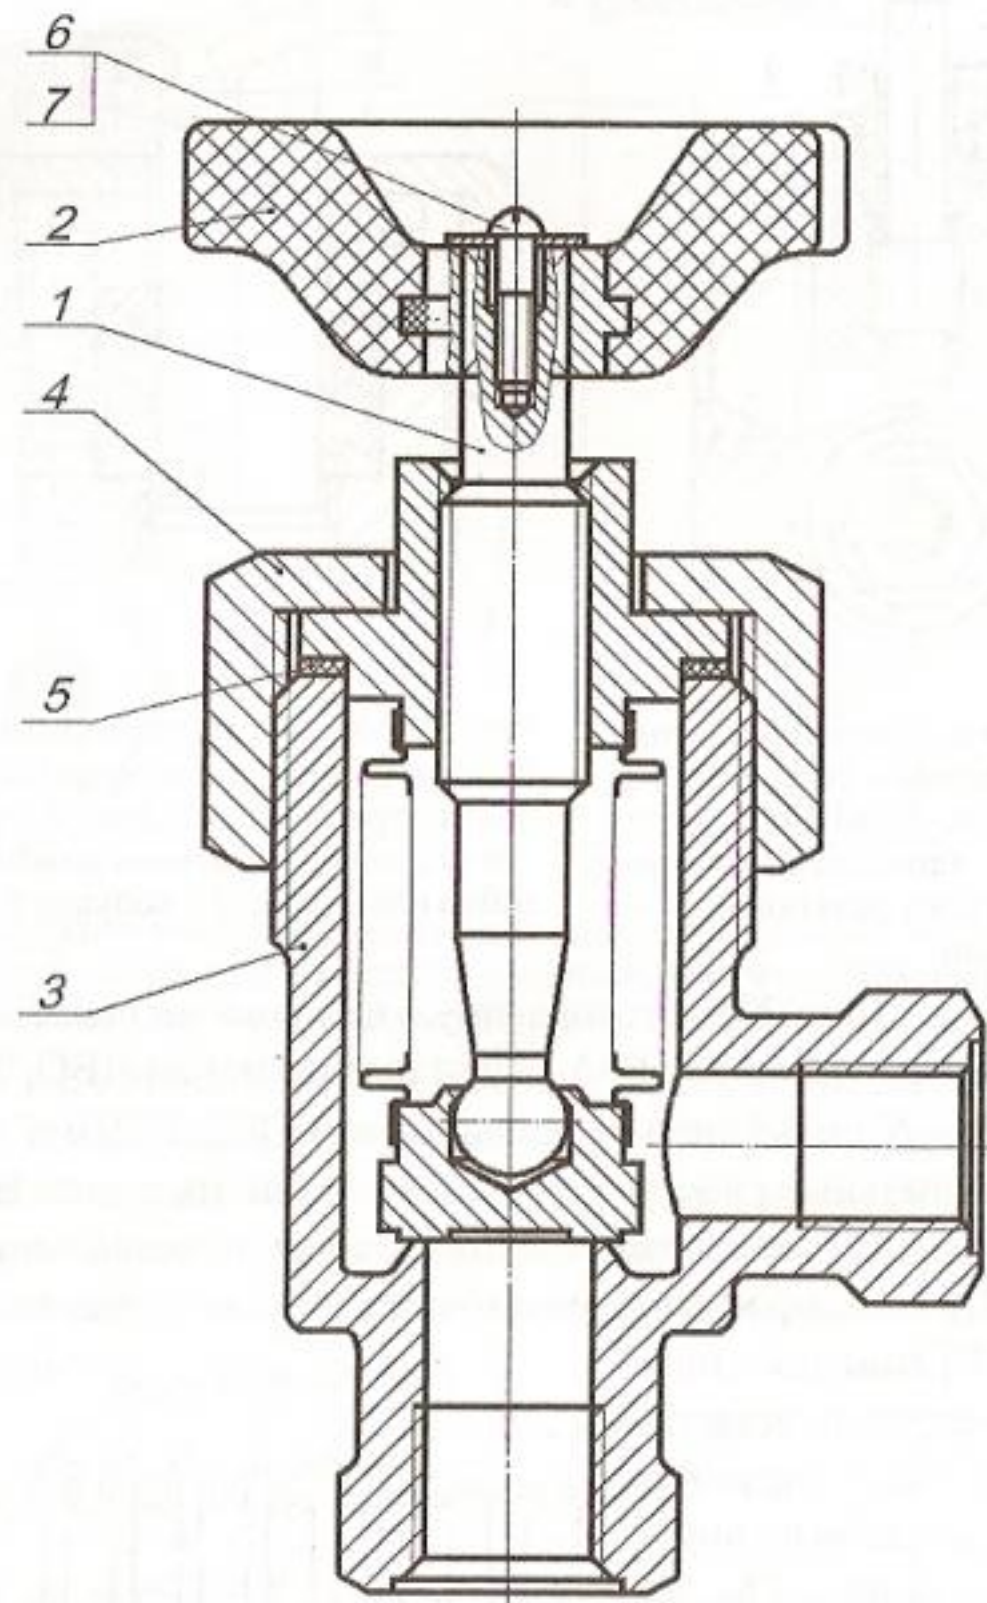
Пример конструкции вентиля с сифонным уплотнением шпинделя: 1 – узел затвора (затвор, шпиндель, крышка, сифон); 2 – маховик (армированная деталь); 3 – корпус; 4 – гайка накладная; 5 – пружина; 6 – винт; 7 – шайба.
